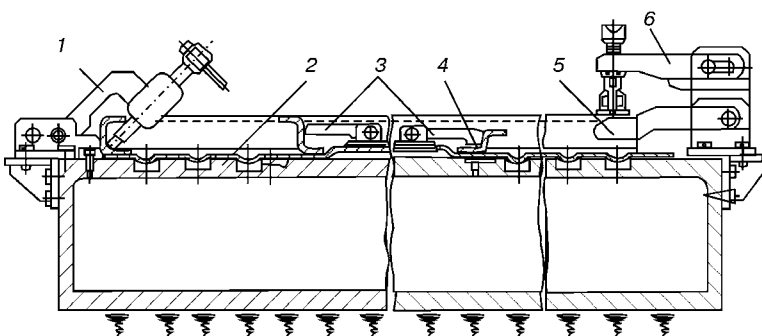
Схема станда для сборки и сварки модулей боковых стенок (обозначения см. в тексте)
